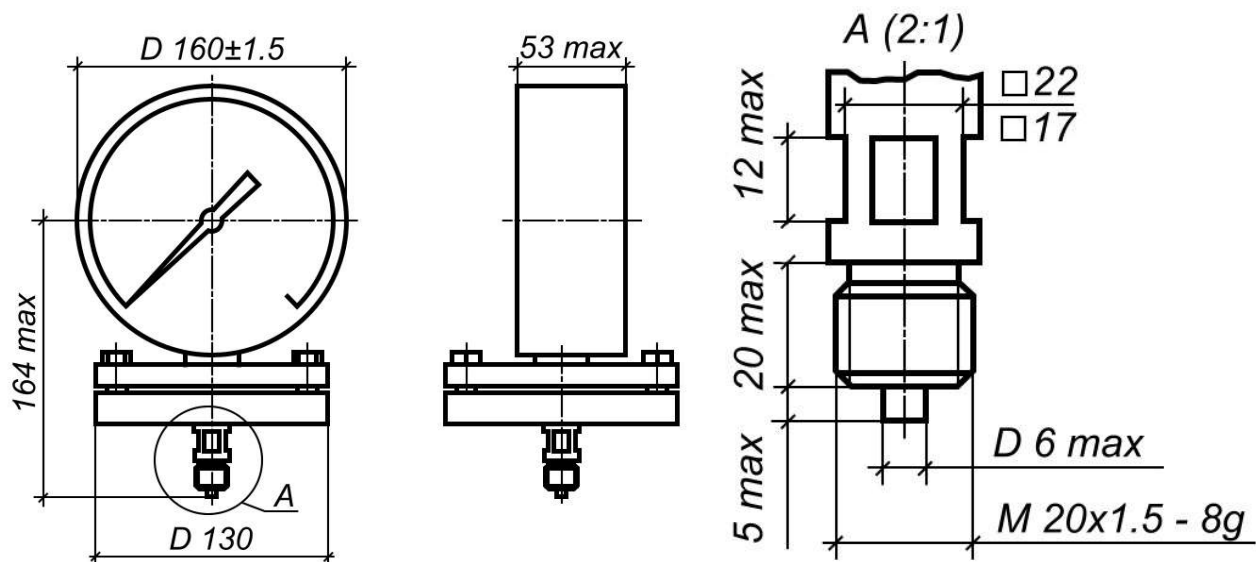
Габаритные и присоединительные размеры приборов исполнения 1
